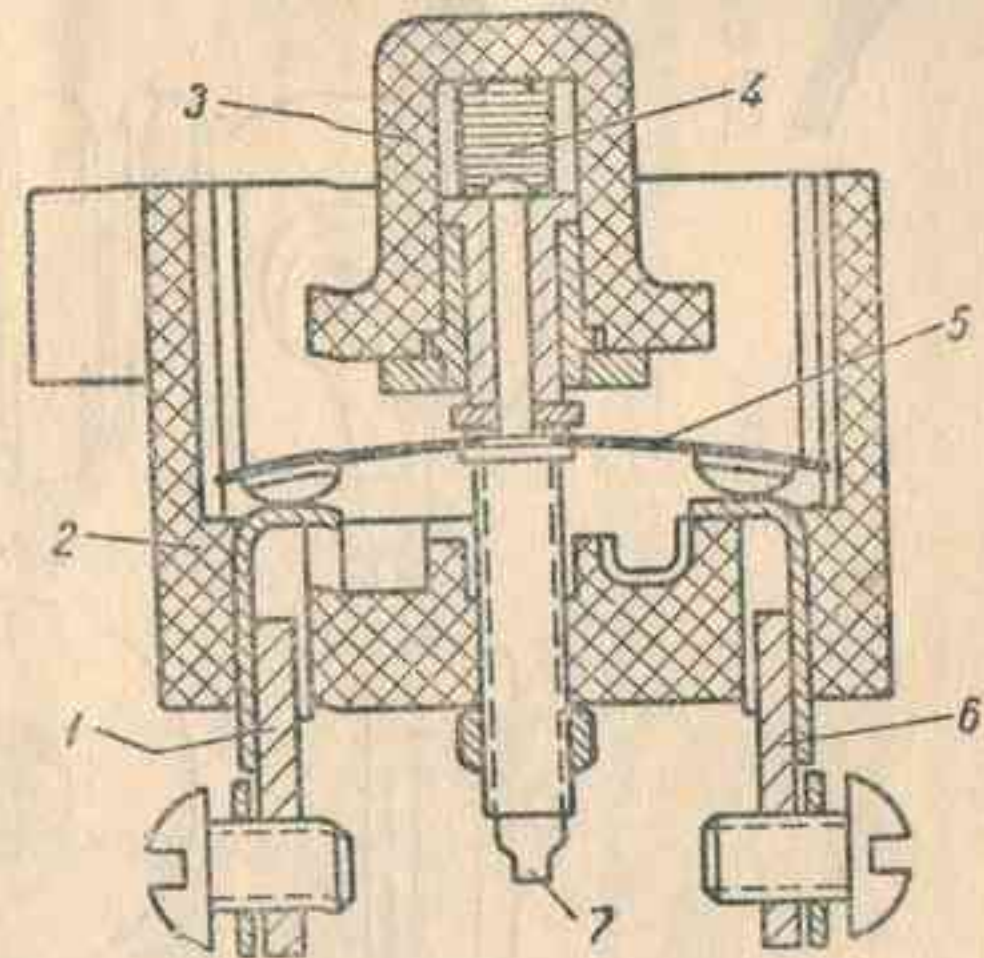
Предохранитель в цепи сигнала: 1 и 6 — неподвижные контакты; 2 — корпус; 3 — кнопка; 4 — пружина кнопки; 5 — биметаллическая пластина с контактами; 7 — стержень (регулирующий винт предохранителя)
